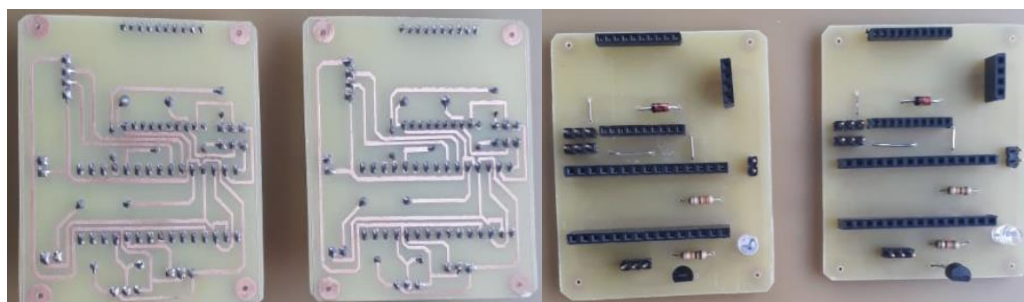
Construcción de la placa electrónica *Printed Circuit Board* (PCB) Para el Nodo 2 y Nodo 3
